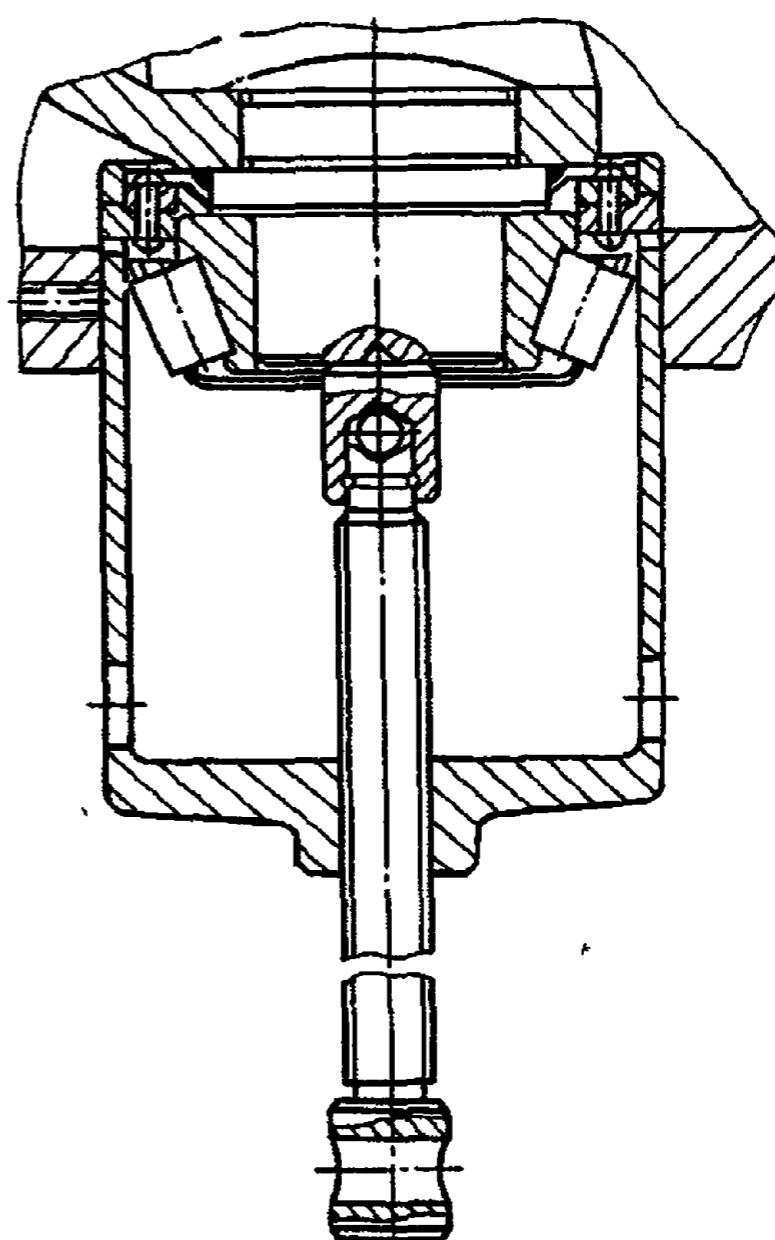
Выпрессовка подшипника шкворня переднего моста
